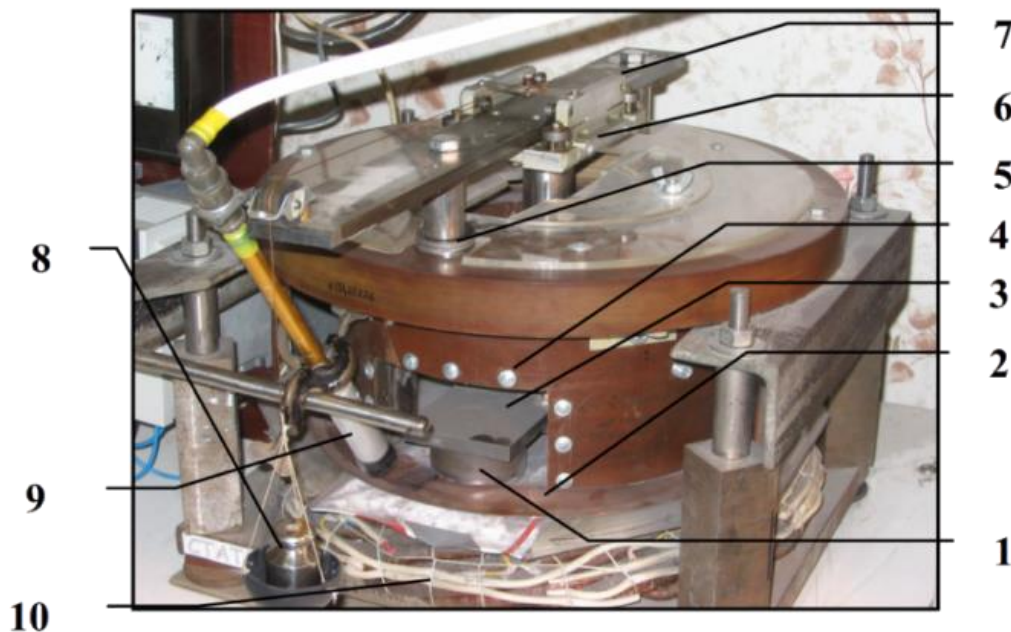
Экспериментальная установка бесшпиндельного станка резки с кольцевым ротором – инструментом без механических опор
